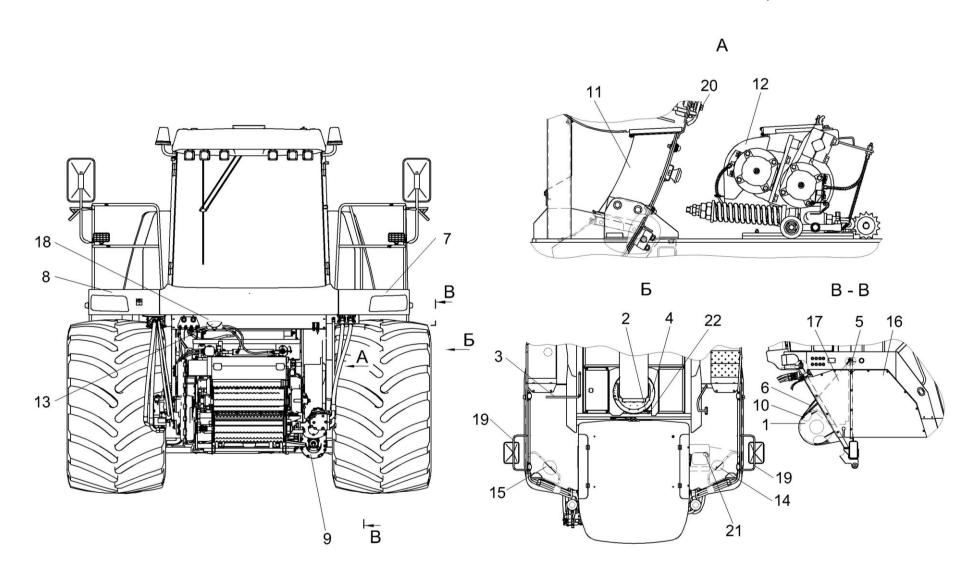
Измельчитель самоходный КВК 0100000-01 (вид спереди)
